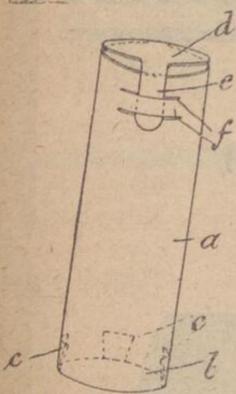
zeigt den ausgestanzten Theil mit anhängendem Boden und Deckel, und Bild 2 eine fertige Schachtel mit zum Theil geschlossenem Deckel.
